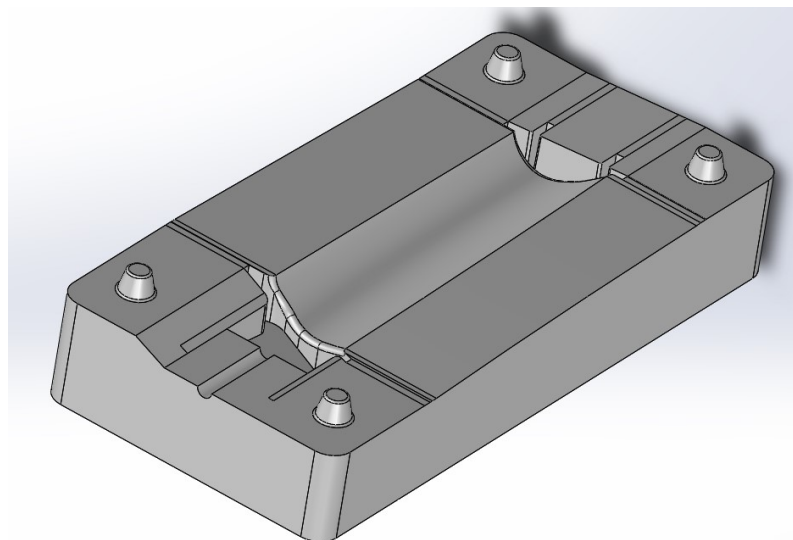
Pinos de guiamento introduzidos no molde da pá de turbina
